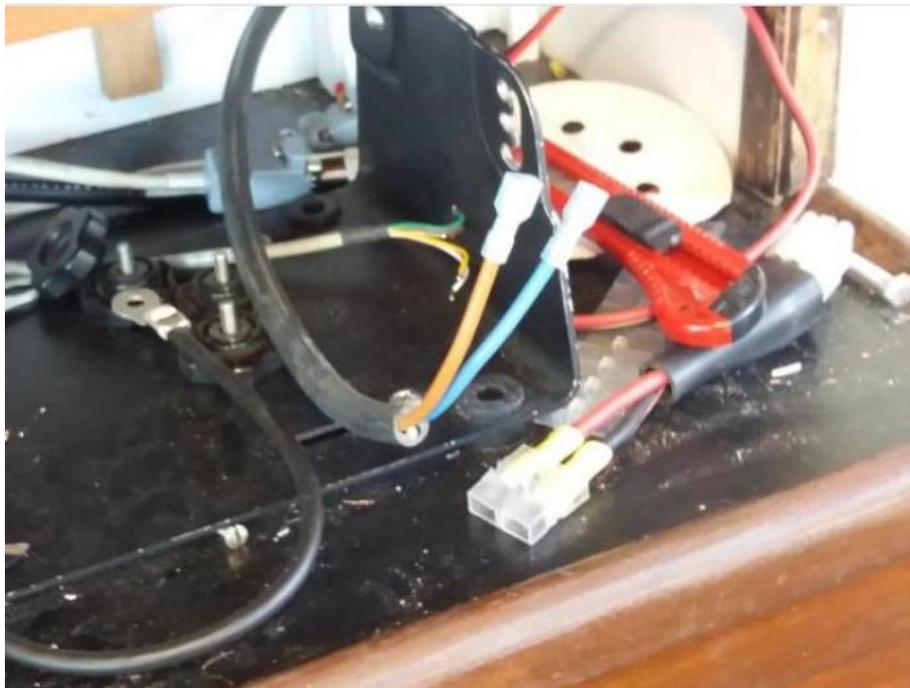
Conectores faston. Fuente: Trabajo de campo.
